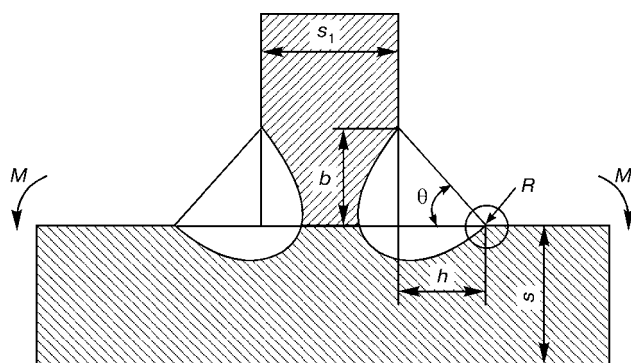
Геометрические параметры углового шва сварного таврового соединения (M – момент приложенной нагрузки; s, s_1 – толщина соответственно свариваемой и привариваемой пластины; b, h – катеты углового шва)
